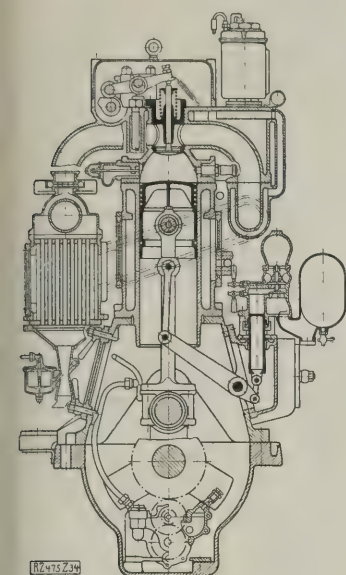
Schnitt durch einen Zylinder des 72 PS-Penta-Motors.
